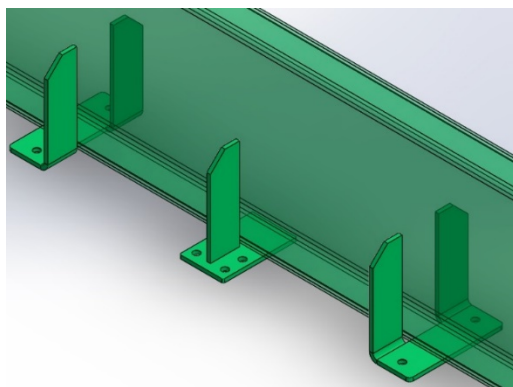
Detalle de los componentes de anclaje de la viga
